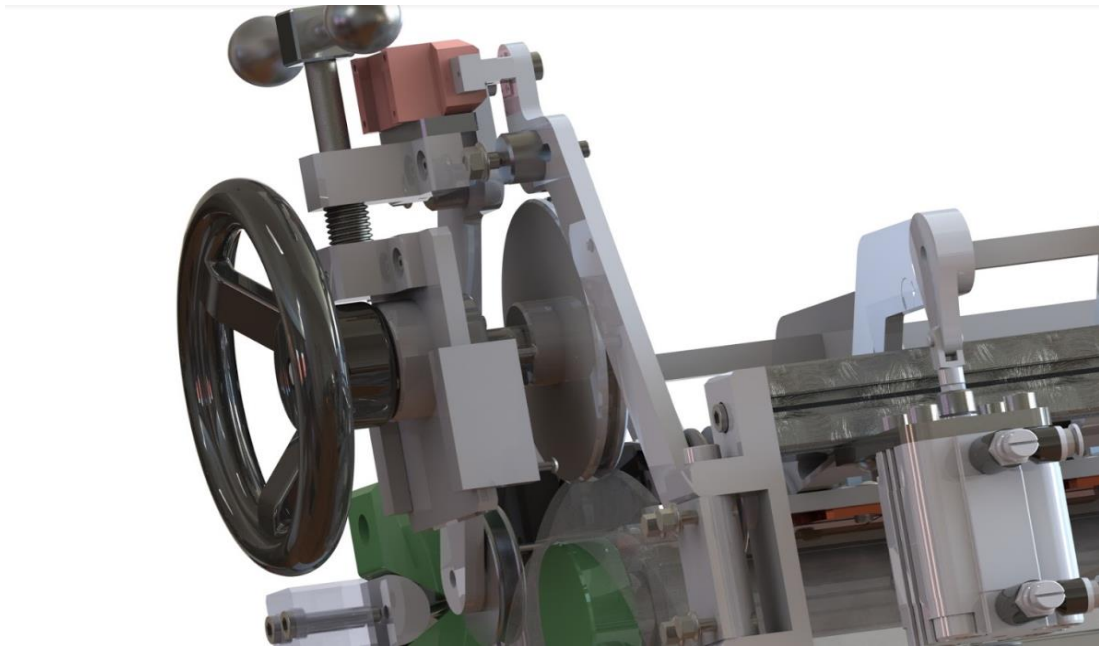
Detalle del sistema de arrastre y ajuste de presión para la soldadura orbital.
